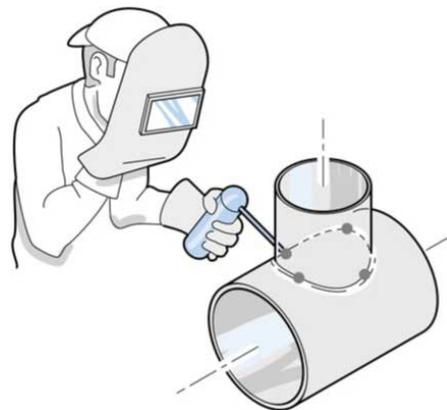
Einschweißmuffe in Rohrleitung einschweißen
